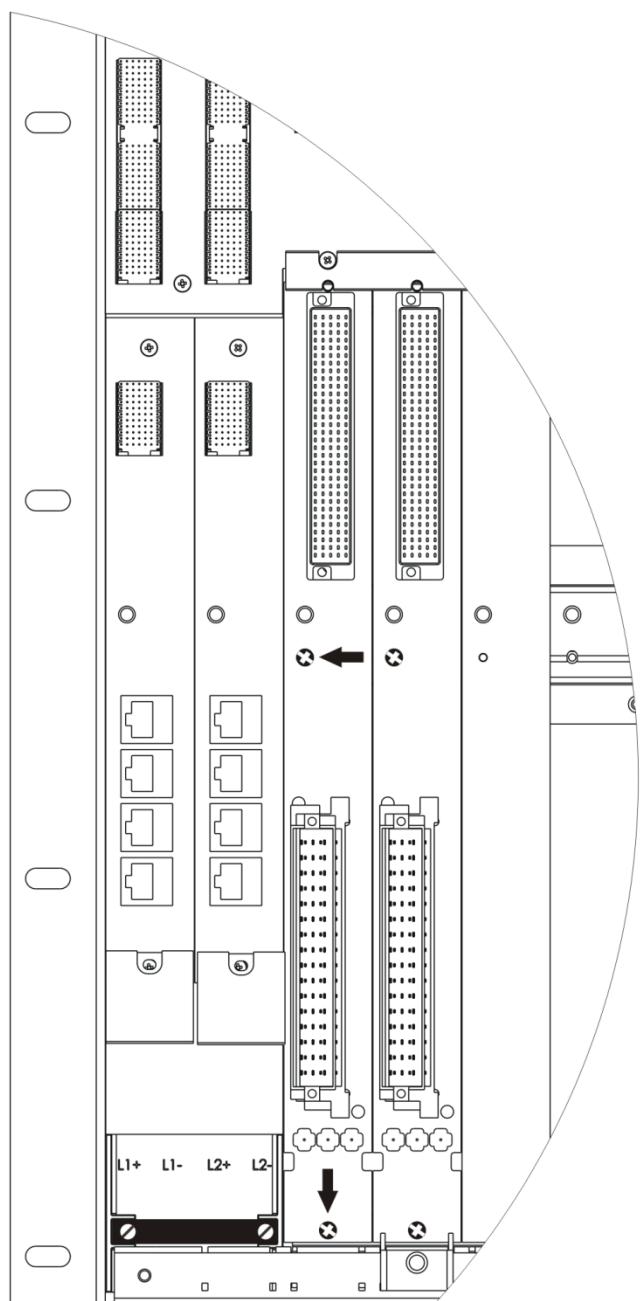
Exemple de fixation par vissage du panneau de raccordement mono
